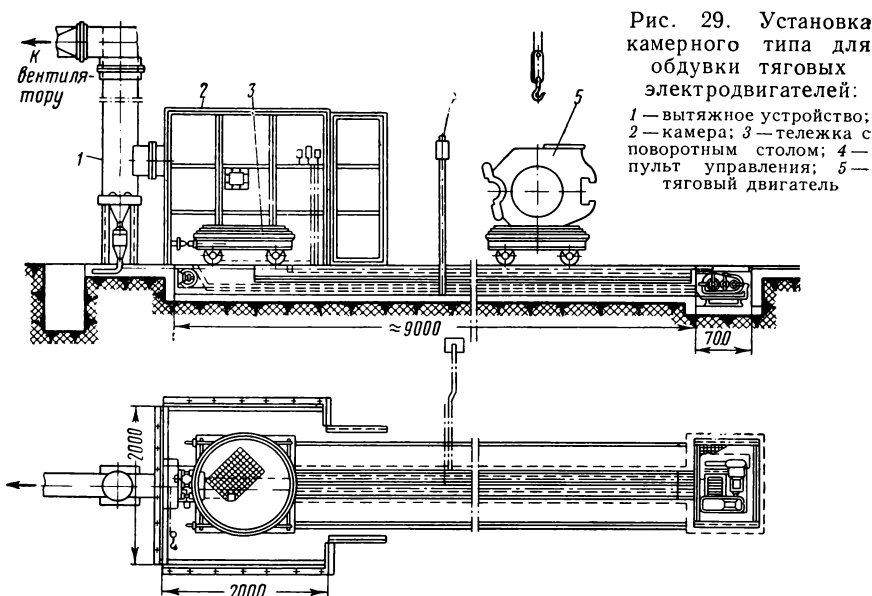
Установка камерного типа для обдувки тяговых электродвигателей:
